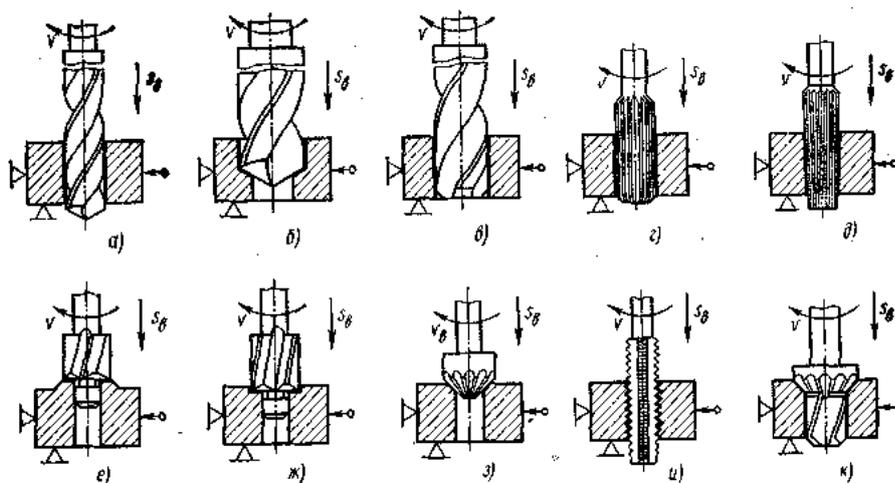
Схема обработки заготовок на вертикально-сверлильных станках
